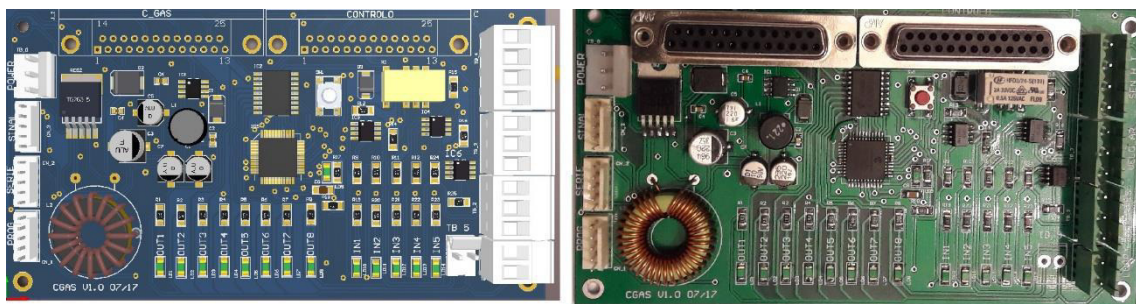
Desenho 3D da PCB CGAS (esquerda) e Fotografia da PCB CGAS terminada (direita)
